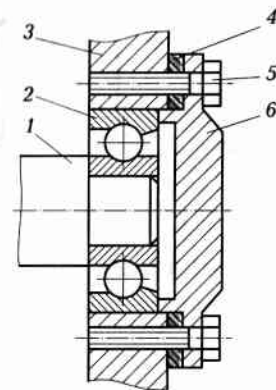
Конструктивная схема опоры с радиально-упорным подшипником: 1 — вал; 2 — подшипник; 3 — корпус; 4 — компенсатор; 5 — болт; 6 — крышка
